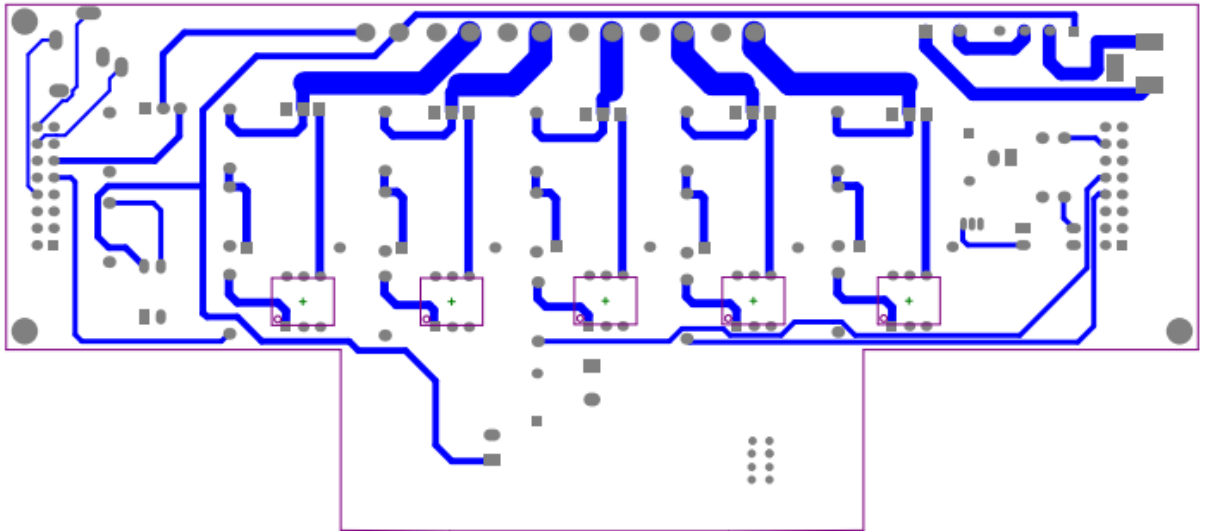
Lớp Bottom PCB mạch điều khiển.
